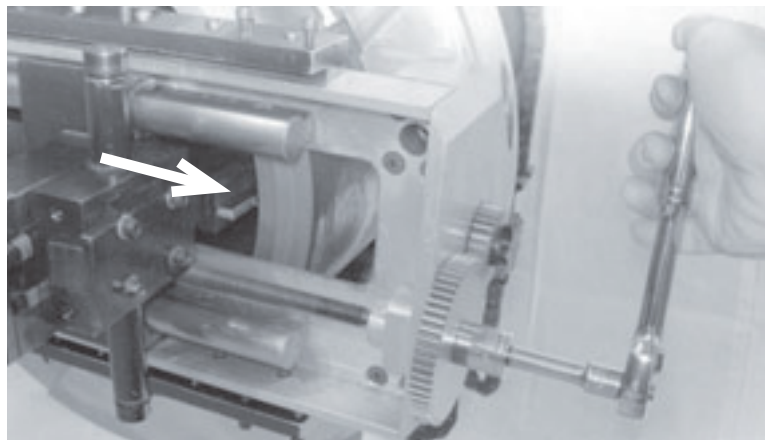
Поворачивайте корончатую гайку против часовой стрелки для подачи резца по направлению к внутреннему диаметру трубы.
